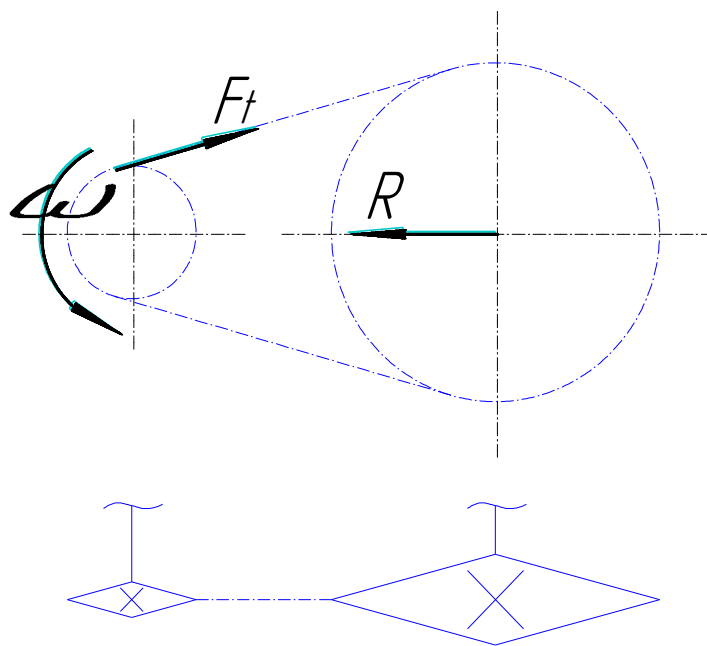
Схема сил, що діють на ланцюгову передачу
